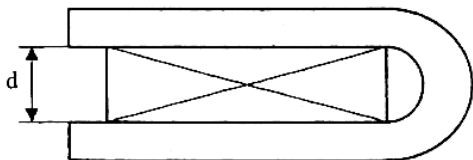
Схема изгиба образцов между двумя нажимными плитами
